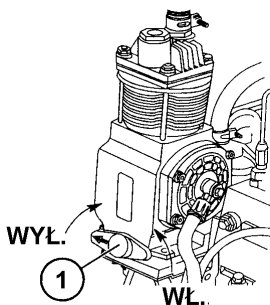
Dźwignia włączania pompy układu hydraulicznego.
